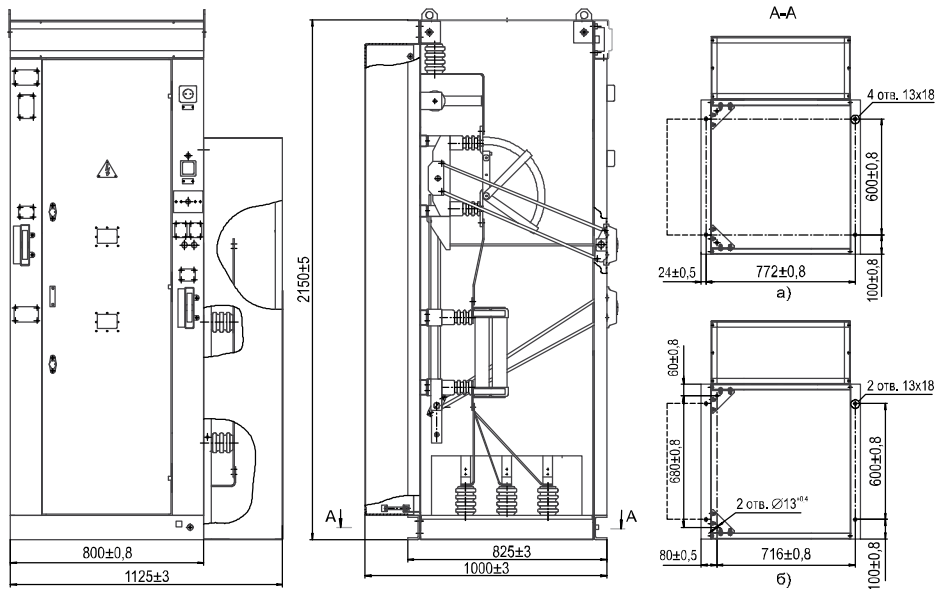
Габаритные, установочные, присоединительные размеры КСО-306 ШВВ:
